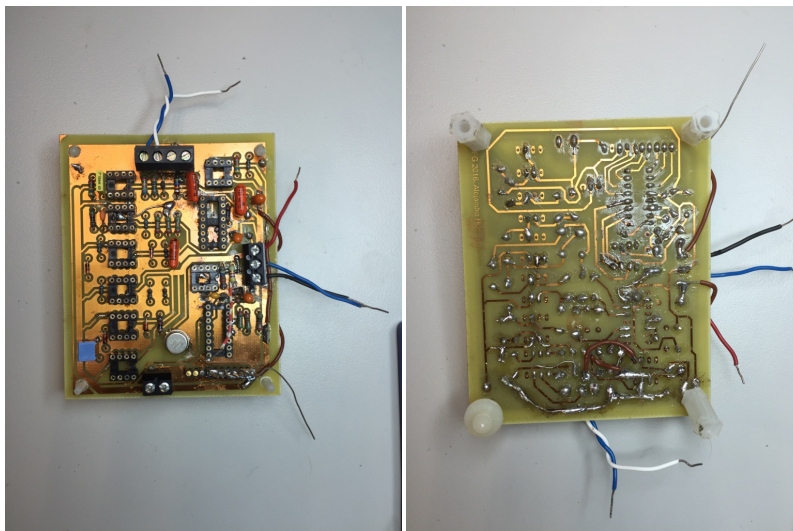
Placa de circuito impreso. A la izquierda, cara Top. A la derecha, cara Down.
